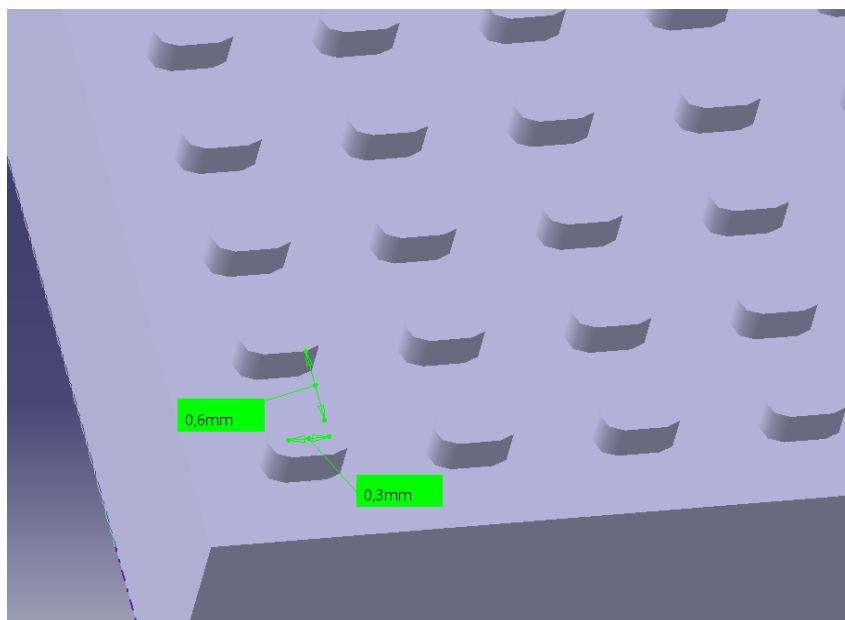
Povrch pravidelných teček o průměru 0,3 mm a mezeře 0,6 mm
